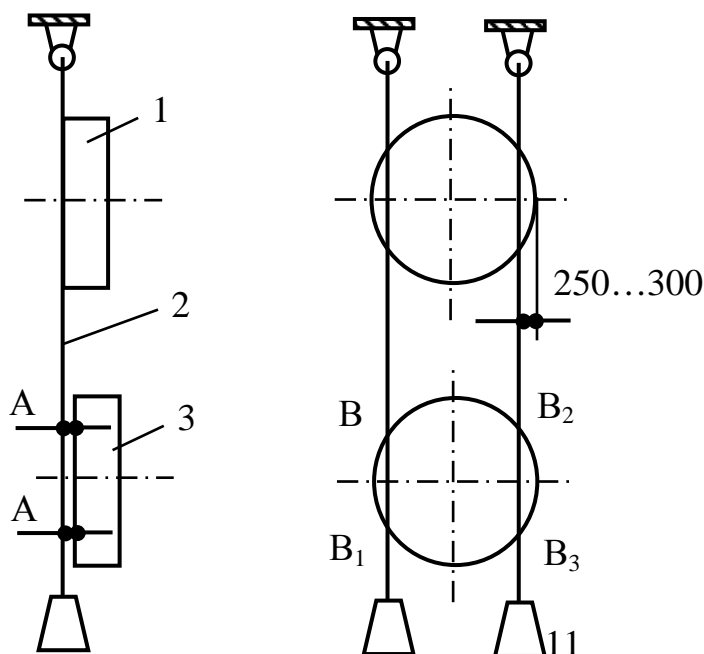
Схема проверки параллельности торцовых поверхностей шкивов
